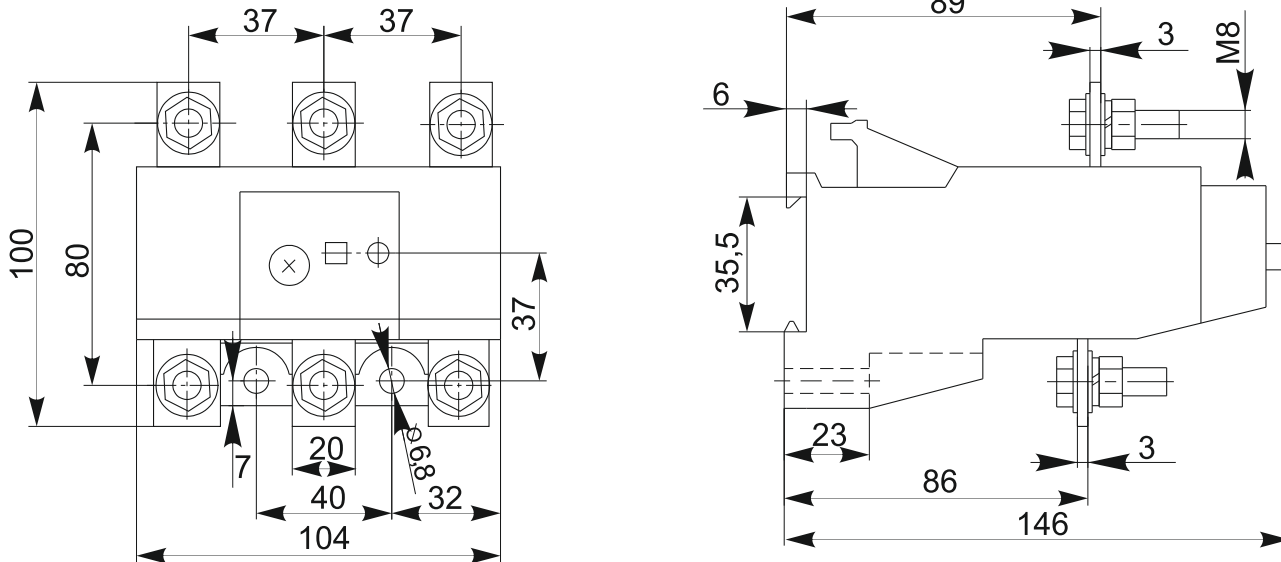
Габаритні, установочні та приєднувальні розміри РТ-4055080, РТ-4063090, РТ-4080110, РТ-4090120, РТ-4110135, РТ-4120150, РТ-4135160, РТ-4150180, варіант 1
